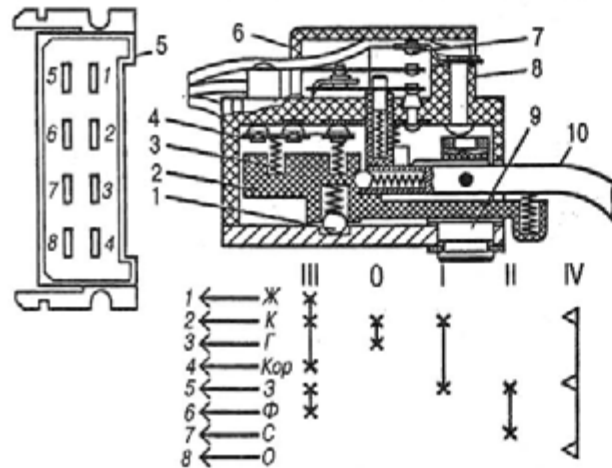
Переключатель стеклоочистителя и его схема: 1 - фиксаторный шарик; 2 - подвижной изолятор; 3 - пружина; 4 - подвижные контакты; 5 - штекерная колодка; 6 - крышка; 7 - неподвижный контакт; 8 - корпус; 9 - ось; 10 - ручка; буква обозначены цвета проводов
